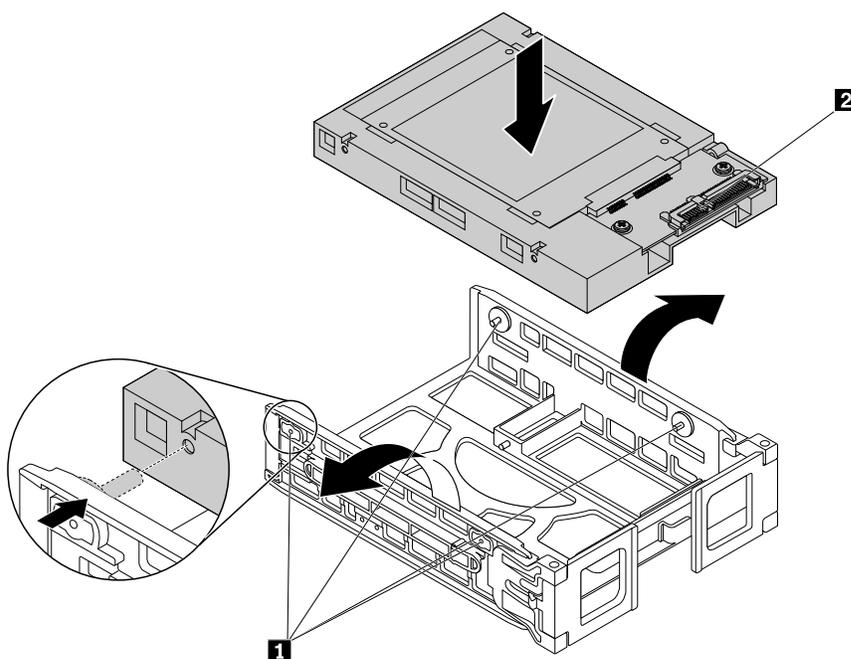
Установка конвертера в крепежную скобу типа 1
